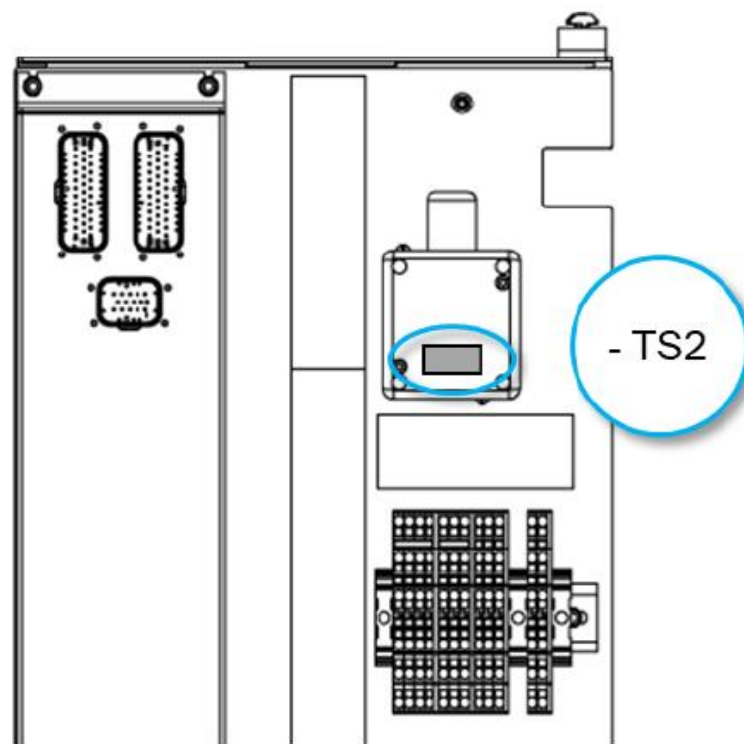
Bauteilkennzeichnung Temperatursensor Innenraum
